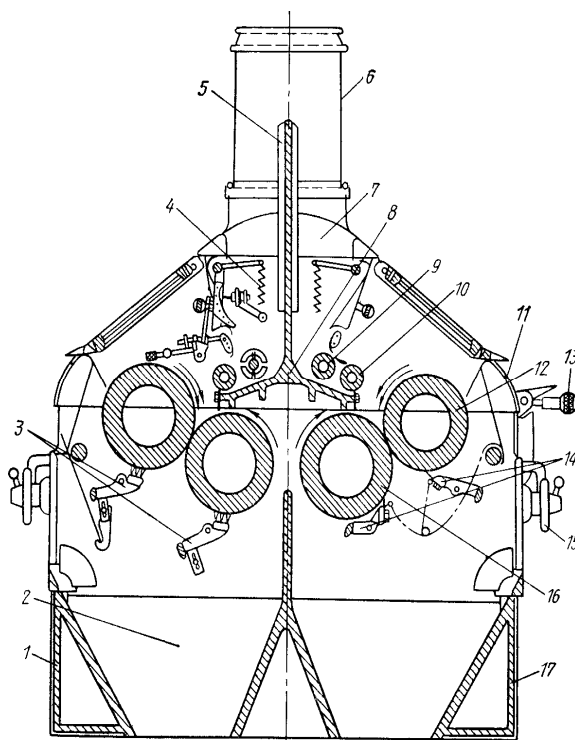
Схема вальцювого верстата А1-БЗН: а – живильний механізм зі шнеком і валиком, рифлені, вальці, що подрібнюють й очищення їх щітками; б – двухваликовий живильний механізм, шорсткуваті вальці й очищення їх шкребками; 1 – боковина станини; 2 – бункер; 3 – щітки; 4 – механізми живлення; 5 – вимірювальний перетворювач системи привалу-відвала; 6 – прийомна труба (циліндр); 7 – горловина; 8 – верхня середня траверса; 9 – задній валик (шнек, валик, що дозує, передавальний вал); 10 – передній валик (дозуючий, або розподільний); 11 – верхня передня панель; 12 – валець, що швидко обертається; 13 – рукоятка ручного привалу і рівнобіжного зближення; 14 – шкребки-ножі для очищення вальців; 15 – штурвал механізму регулювання паралельності; 16 – валець, що повільно обертається; 17 – нижня лицьова траверса.
